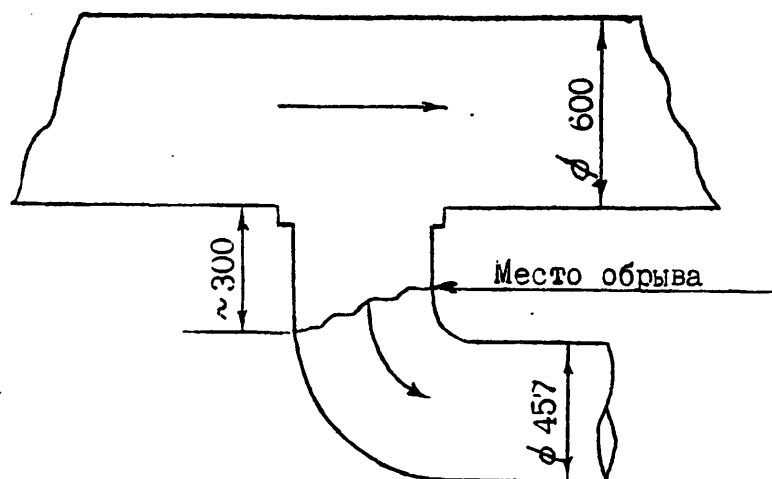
Схема соединения трубопроводов ПВ на АЭС "surry-2"
